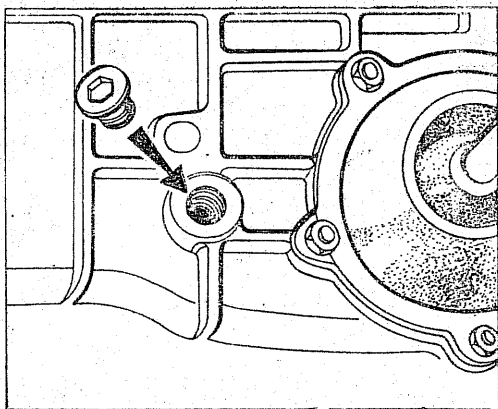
Verschlussschraube für Öleinfüllen und Ölstandmessung im Wechselgetriebe und Achsantrieb
